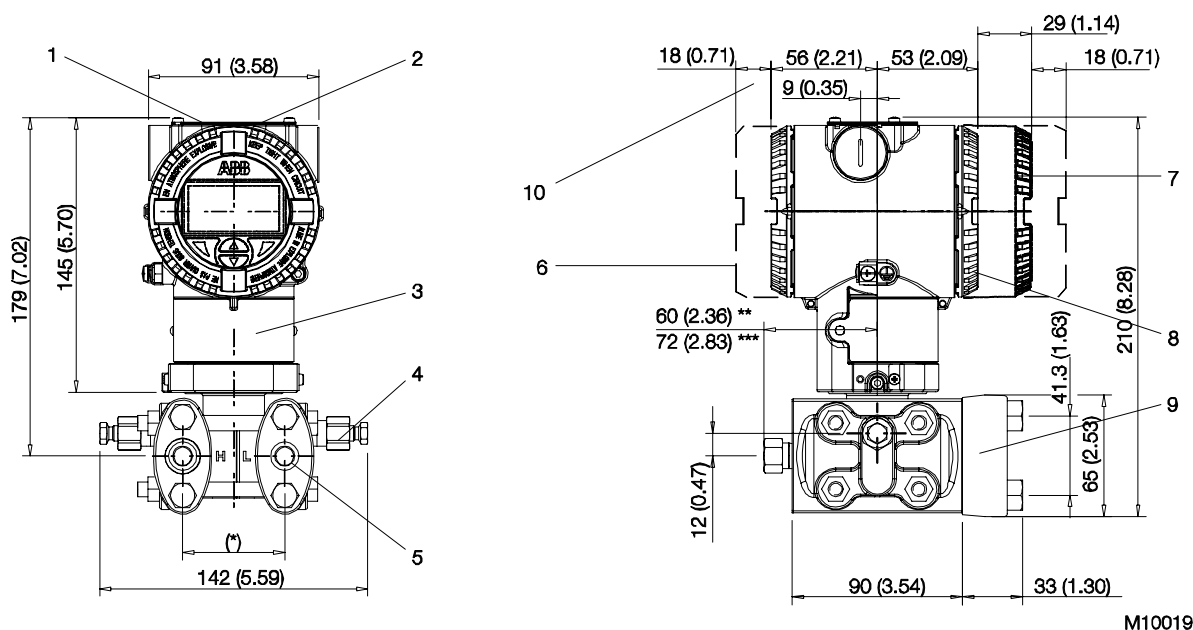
Barrel-Gehäuse - Horizontale Flansche
